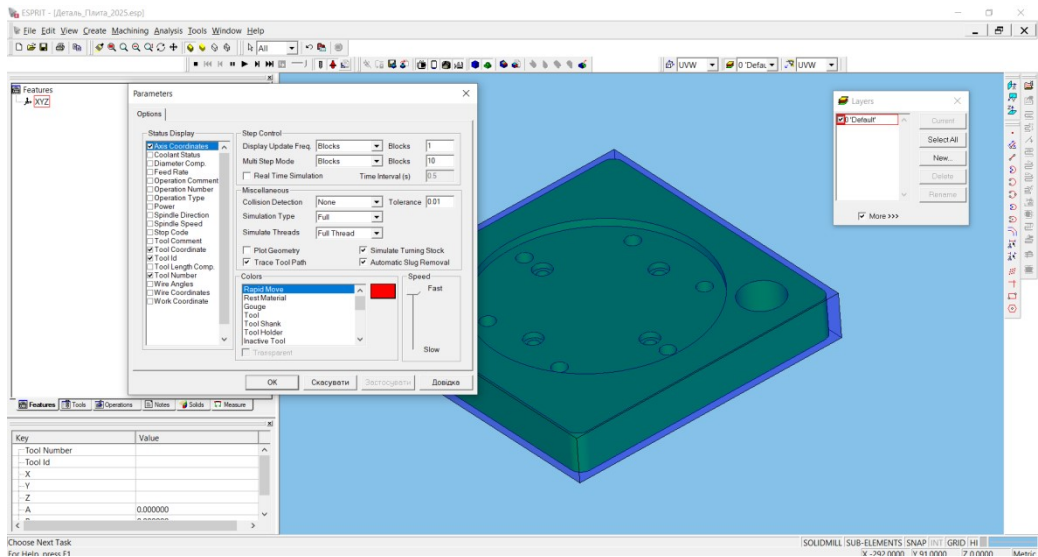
Створення заготовки деталі плита 47.04.05 у САМ Esprit
